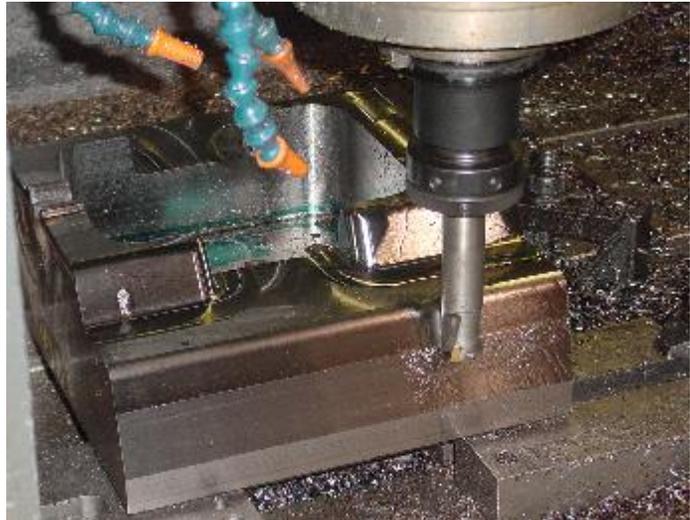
Una centro de maquinado vertical haciendo un maquinado en una pieza de trabajo.
